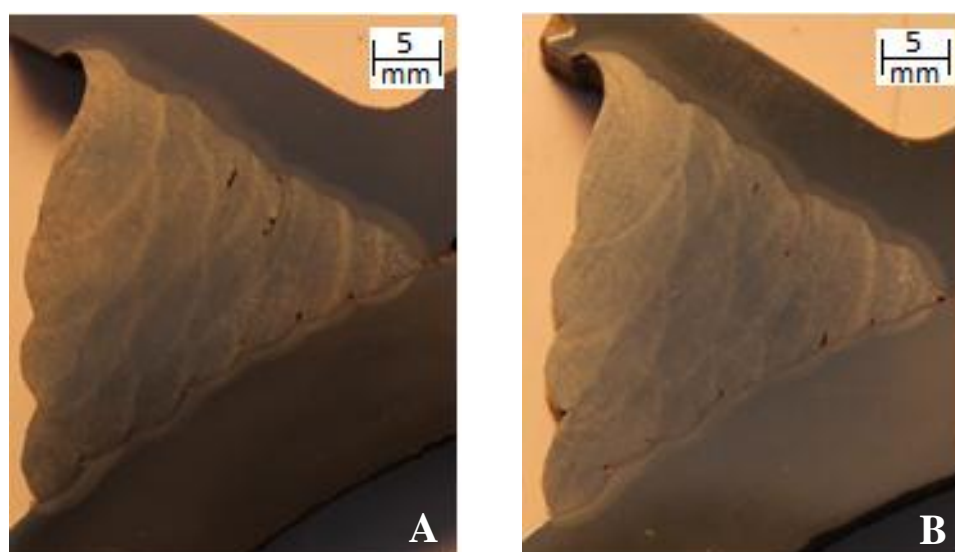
Macrografias do corpo de prova soldado com o processo MIG/MAG convencional na posição horizontal
